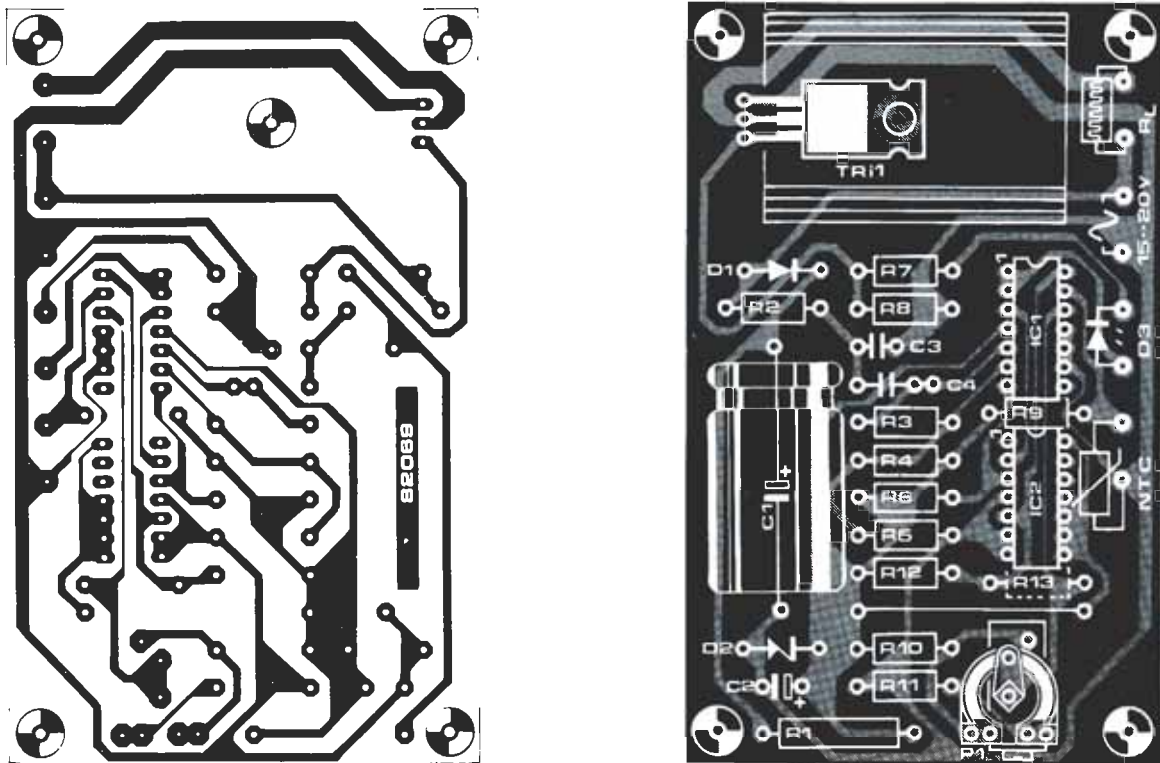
Trazado de las pistas de cobre y disposición de componentes sobre la placa de circuito impreso del termostato.
